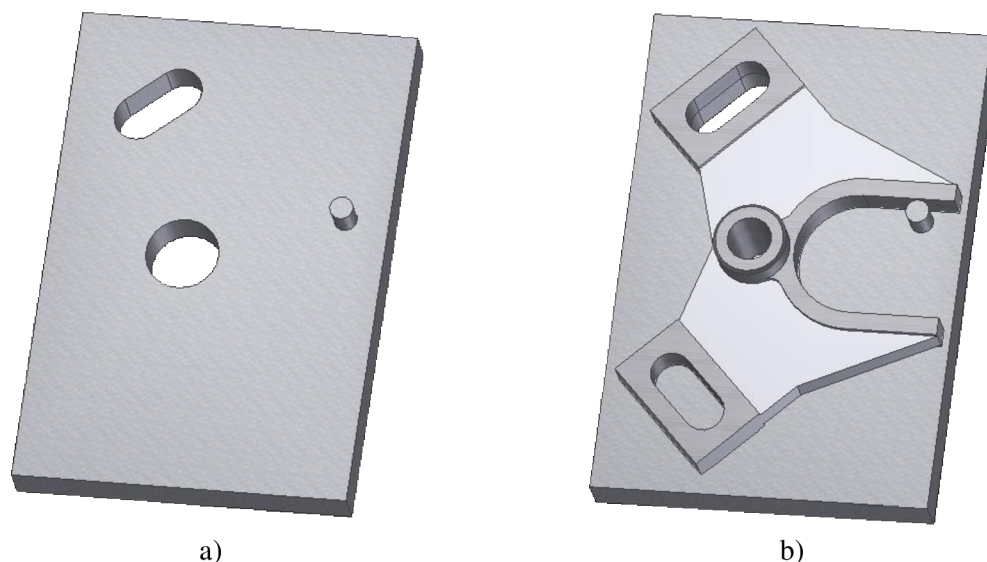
Model přípravku pro frézování drážky  $\text{Ø}42$  mm:
